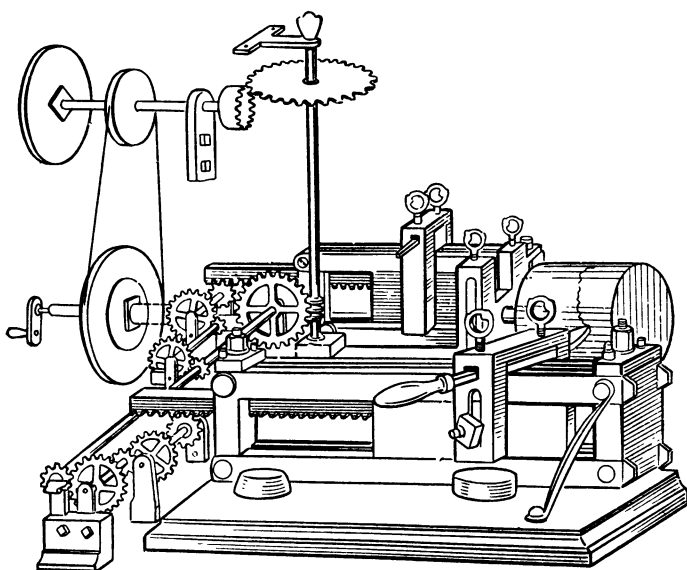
Суппорт «самоходный» токарно-копировального станка А. К. Нартова (1712 г.). Опоры и рамы выполнены из дерева, слева — ручка для вращения ведущего шкива.
